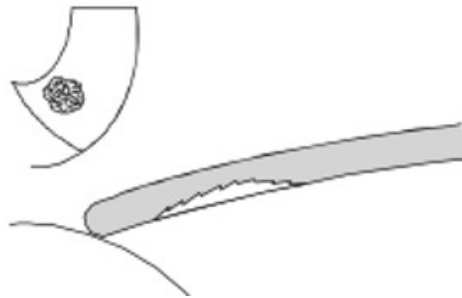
Ubicación Daño por Cavitación Detallado por Gülich [1]
